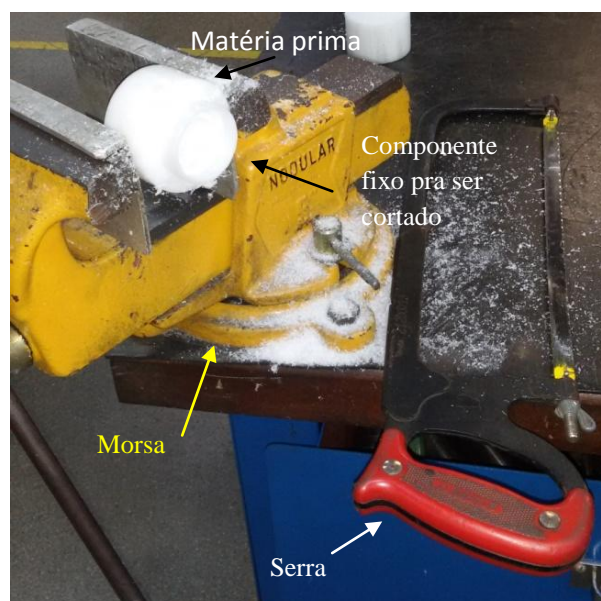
Morsa fixa a mesa usada como suporte para a serra
